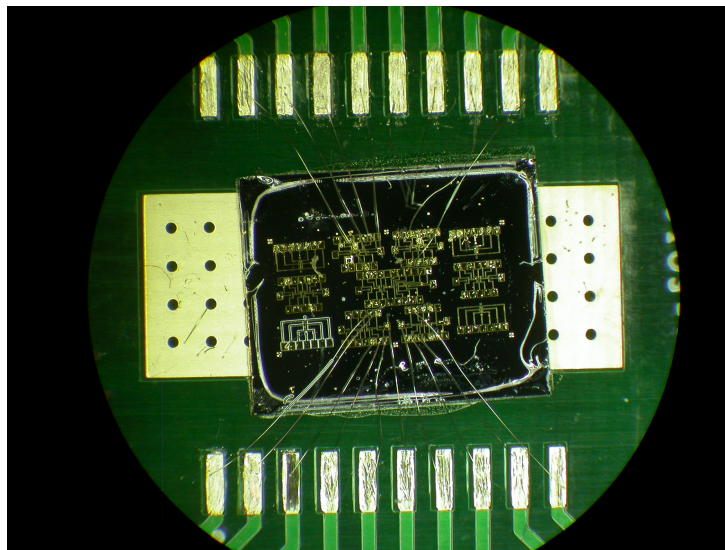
Échantillon collé sur un PCB et micro soudé.
